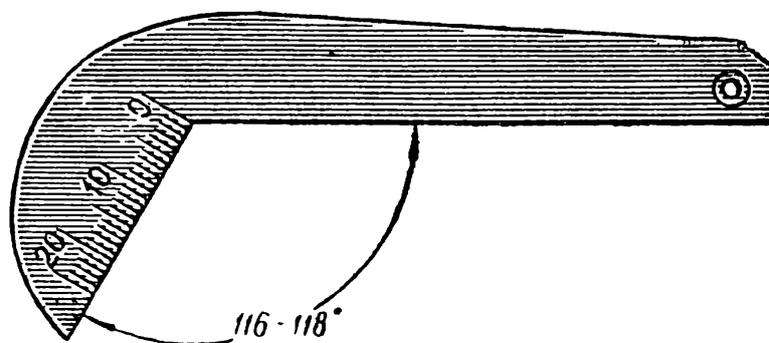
Шаблон для проверки углов сверл при заточке. Миллиметровая шкала служит для проверки центральности заточки
